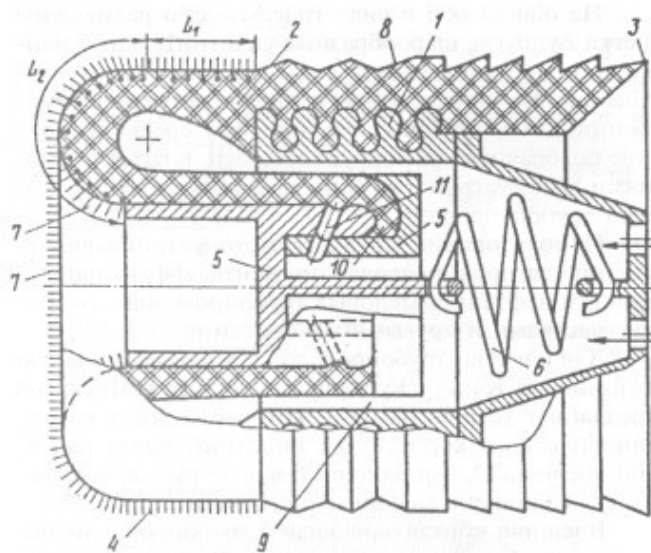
Конструкция саморегулирующегося очистного устройства, где 1 – цилиндрический корпус; 2 – надувная оболочка; уплотняющая кромка; 4 – скребковые элементы; 5 – стакан; 6 – пружина; 7 – дополнительные скребки; 8 – наружная часть оболочки; 9 – канал; 10 – рукав; 11 – сопла.
